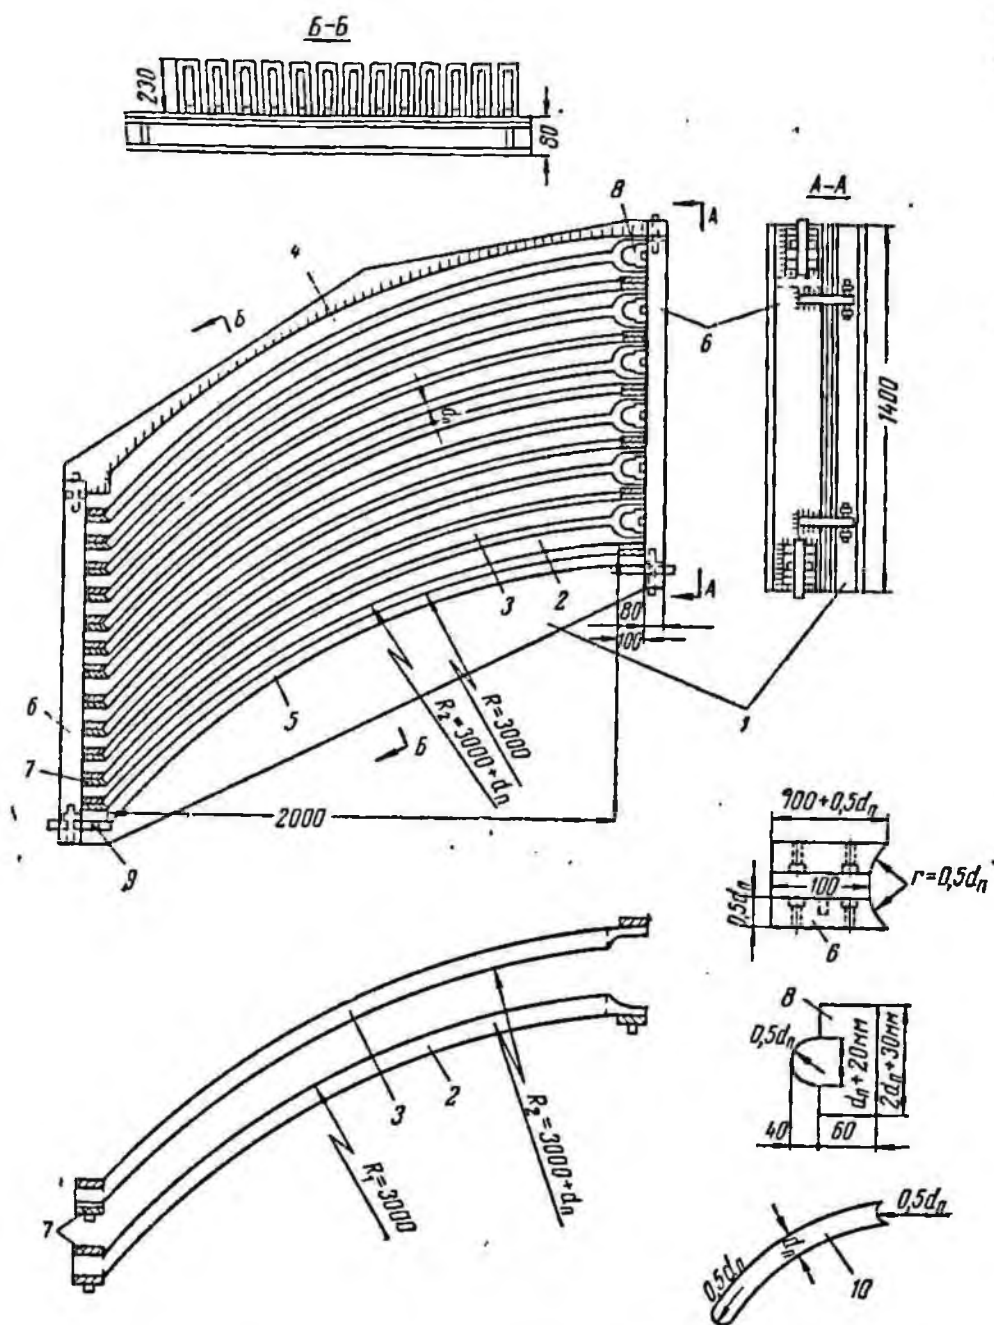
Универсальная пакетная форма для изготовления крепи ТАГ
